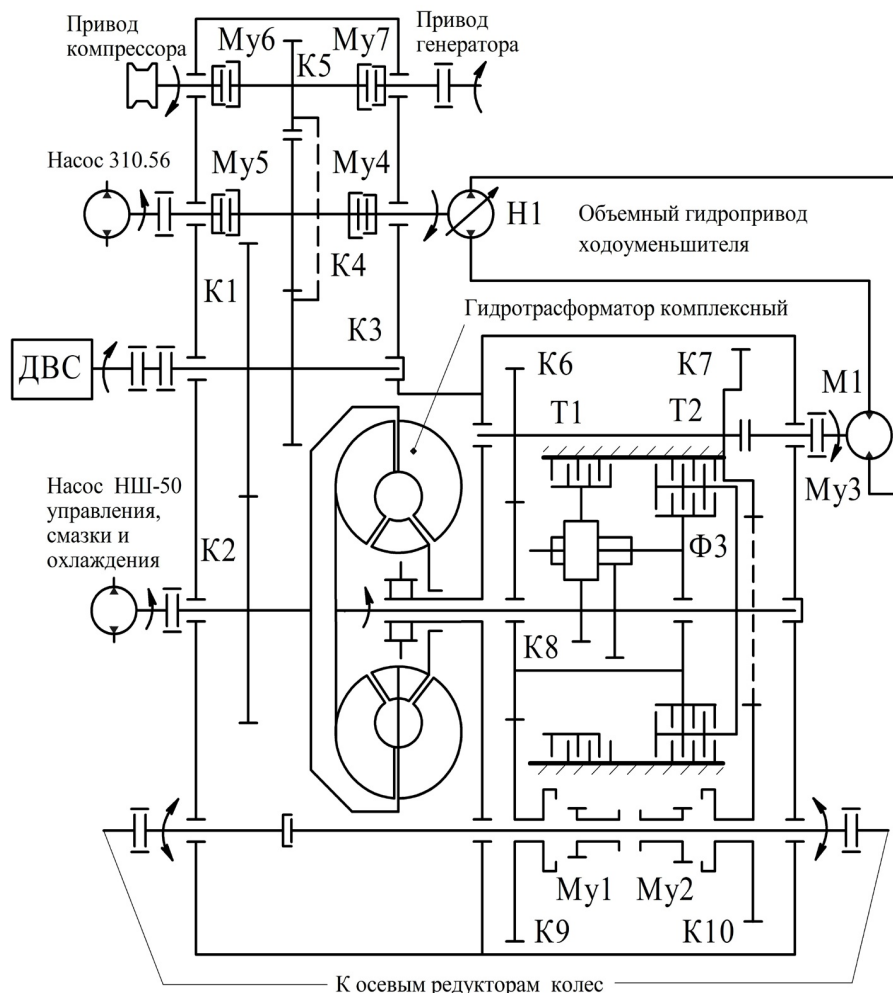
Схема гидромеханической передачи ГП-300: К1—К10 — зубчатые колеса; My1—My7 — управляемые зубчатые муфты; Т1, Т2 и Ф3 — фрикционы
